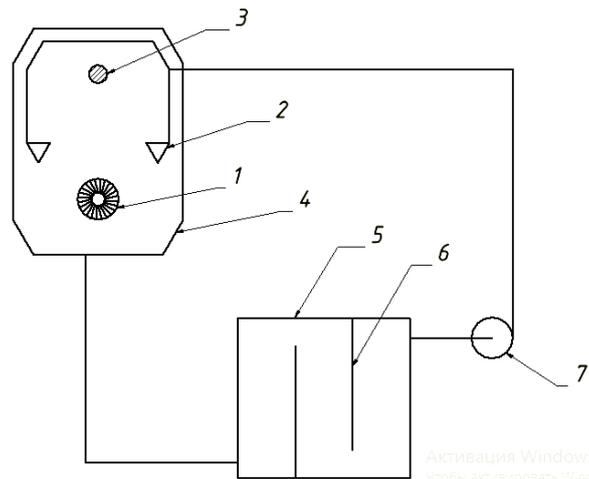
Схема установки для обезжиривания и промывки внутренней поверхности нижних головок шатунов: 1 - щётка, 2 - форсунка, 3 – оправка для закрепления, 4 - корпус, 5 – переливной отстойник, 6 – перегородка, 7 - насос
